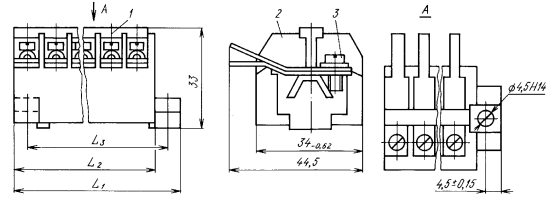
Габаритные, установочные и присоединительные размеры блоков зажимов с выводами "винт - пайка":
